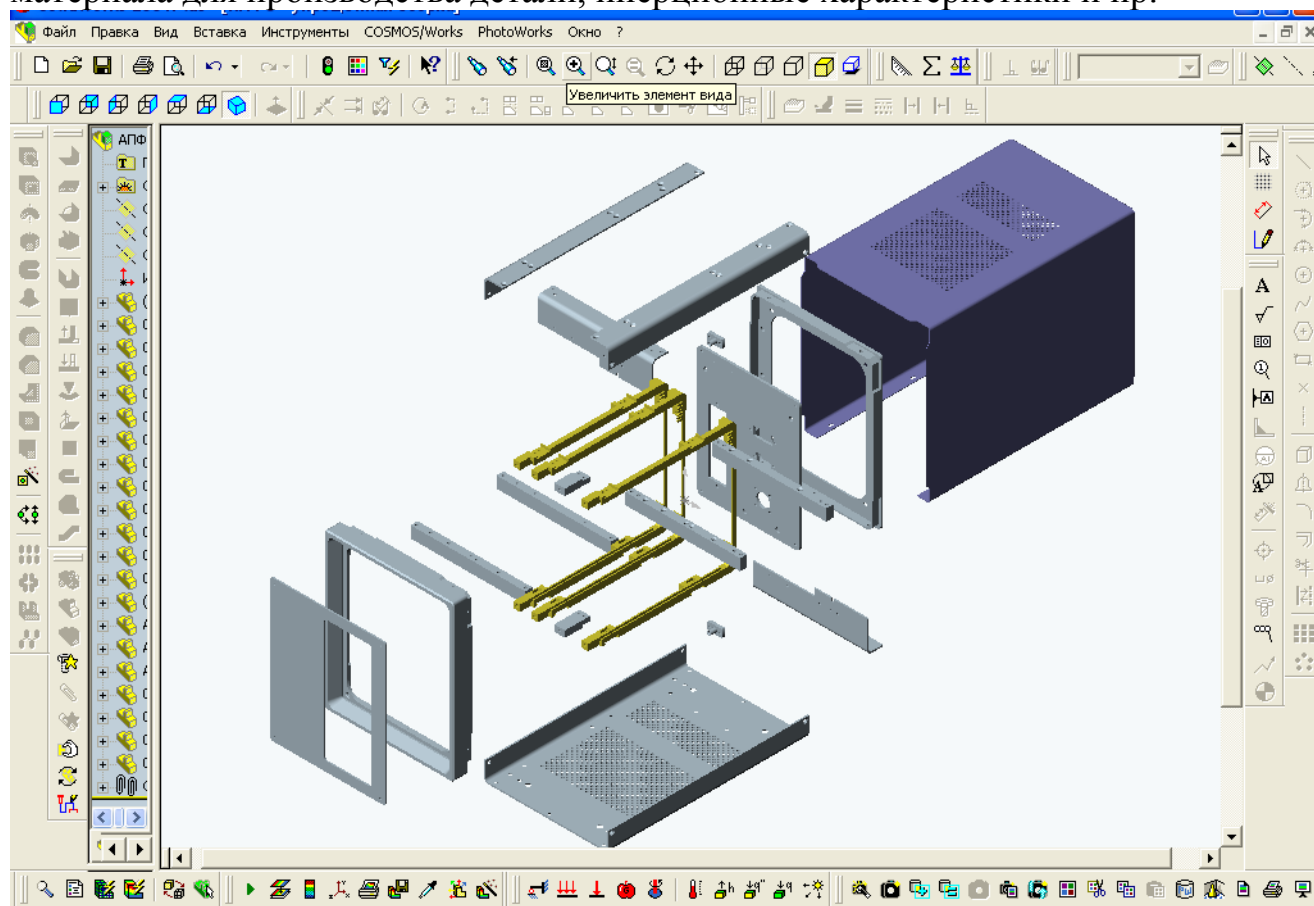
«Вид с разнесенными частями» - пошаговая сборка изделия в САПР SolidWorks
